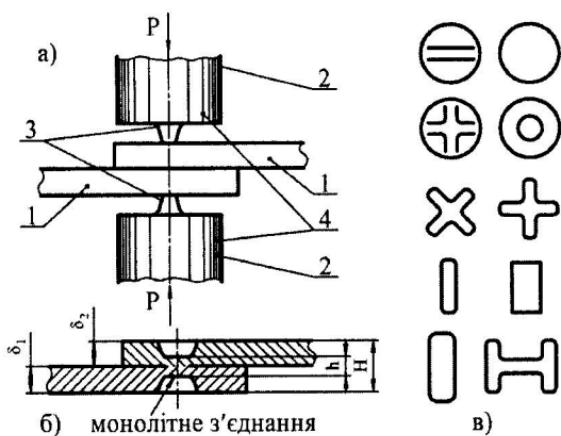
Схема холодного точкового зварювання (а), геометрія зварного з'єднання (б) і форми пуансонів (в)
